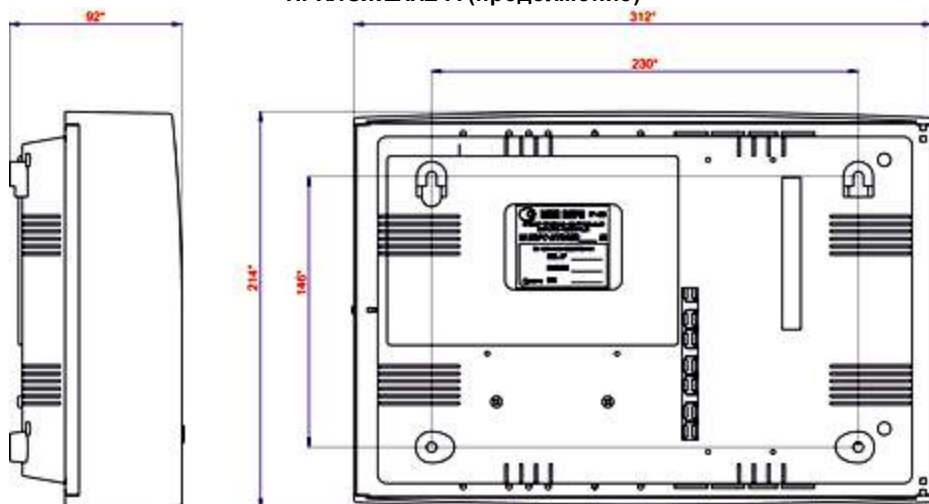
Габаритные и установочные размеры прибора ВЭРС-HYBRID.
